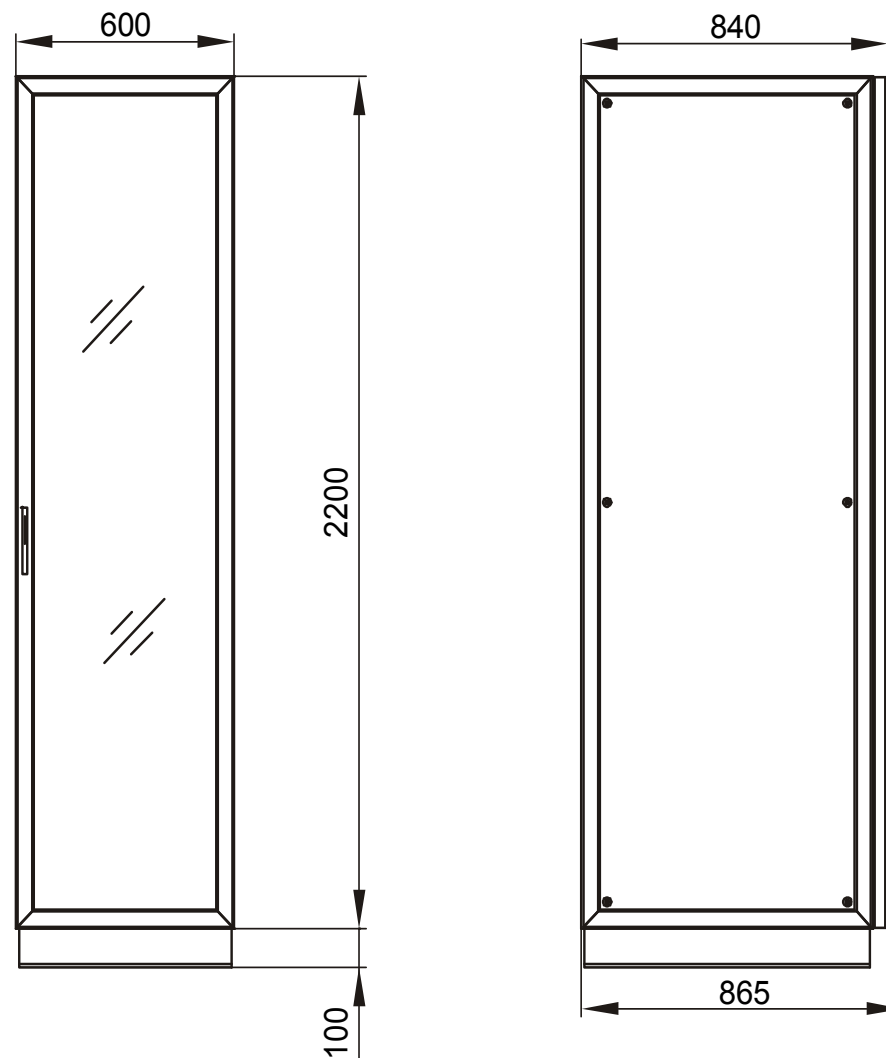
Внешний вид и габаритные размеры пульта ПОСТ-1
